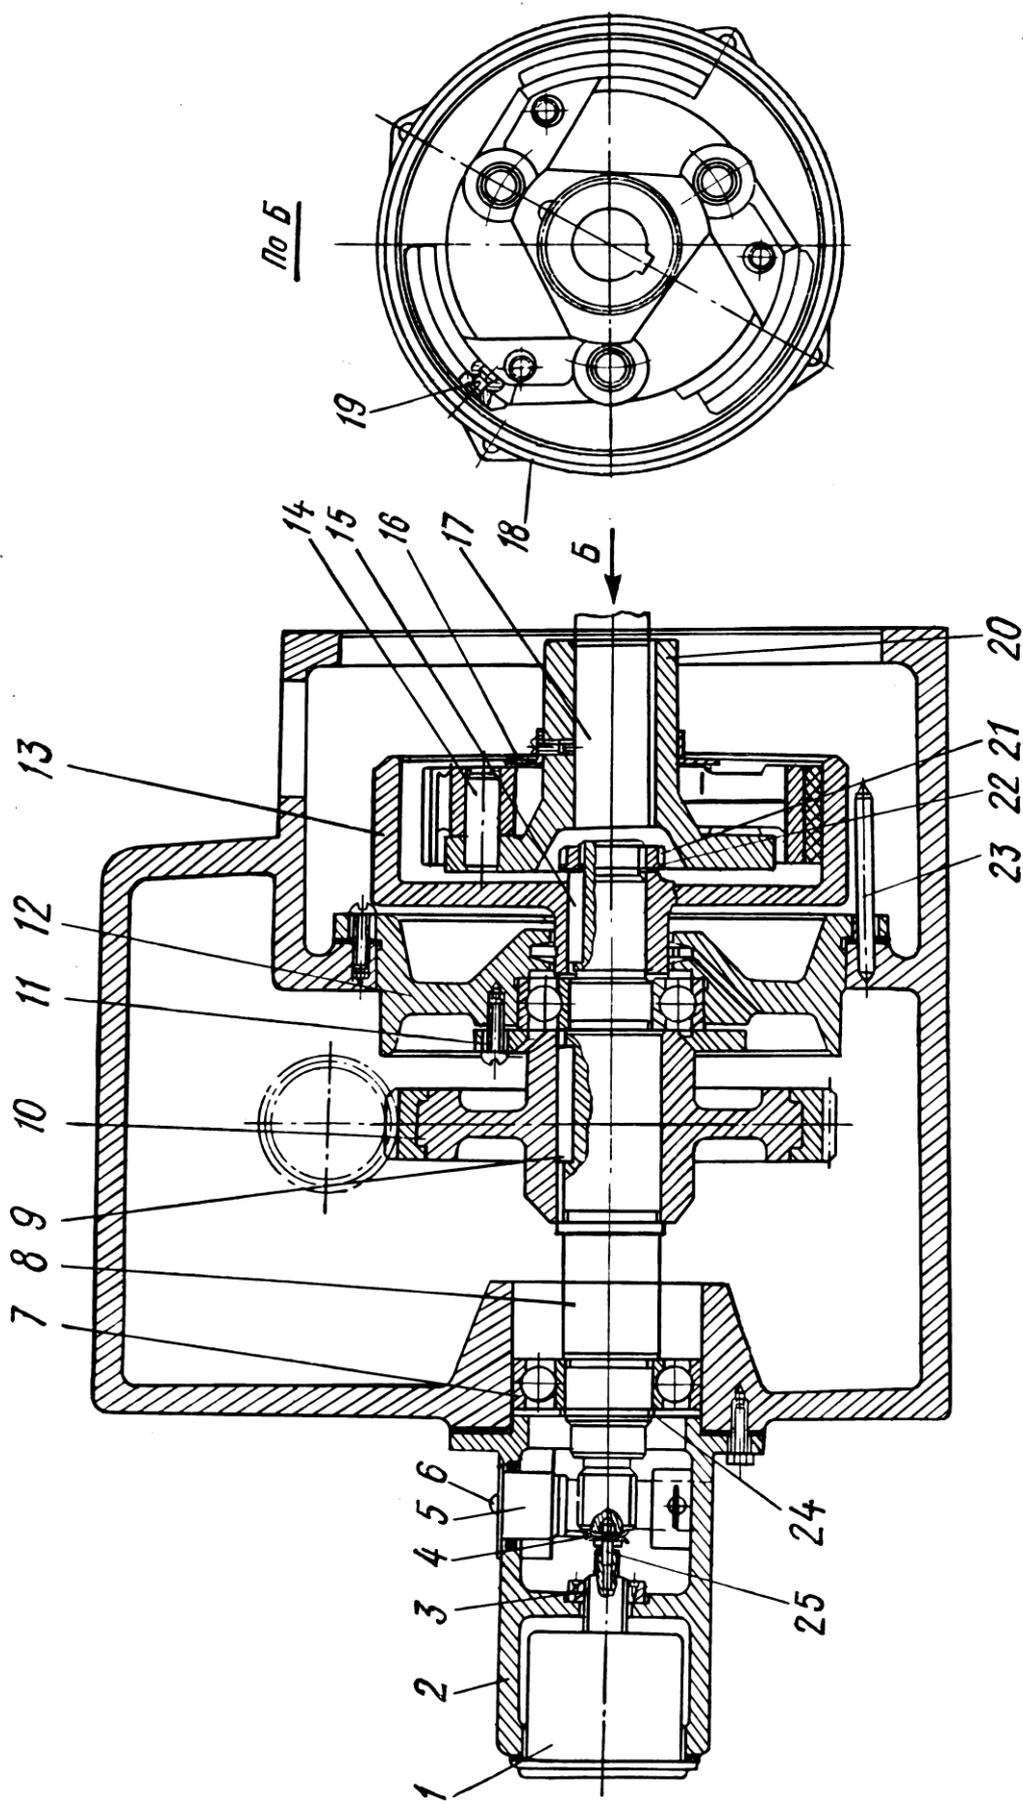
Горизонтальный вал сепаратора Г9-ОСП: 1 – тахометр; 2 – корпус тахометра; 3, 21 – гайки; 4 – шплинт; 5 – шестерня указателя оборотов; 6 – вал; 7 – шарикоподшипник; 8 – вал; 9, 15 – шпонки; 10 – шестерня; 11 – крышка; 12 – фланец; 13 – бандаж; 14 – палец; 16 – ограничитель; 17 – вал электродвигателя; 18 – упор; 19 – заклепка; 20 – диск; 22 – запорная шайба; 23 – шпилька; 24 – кольцо; 25 – поводок
